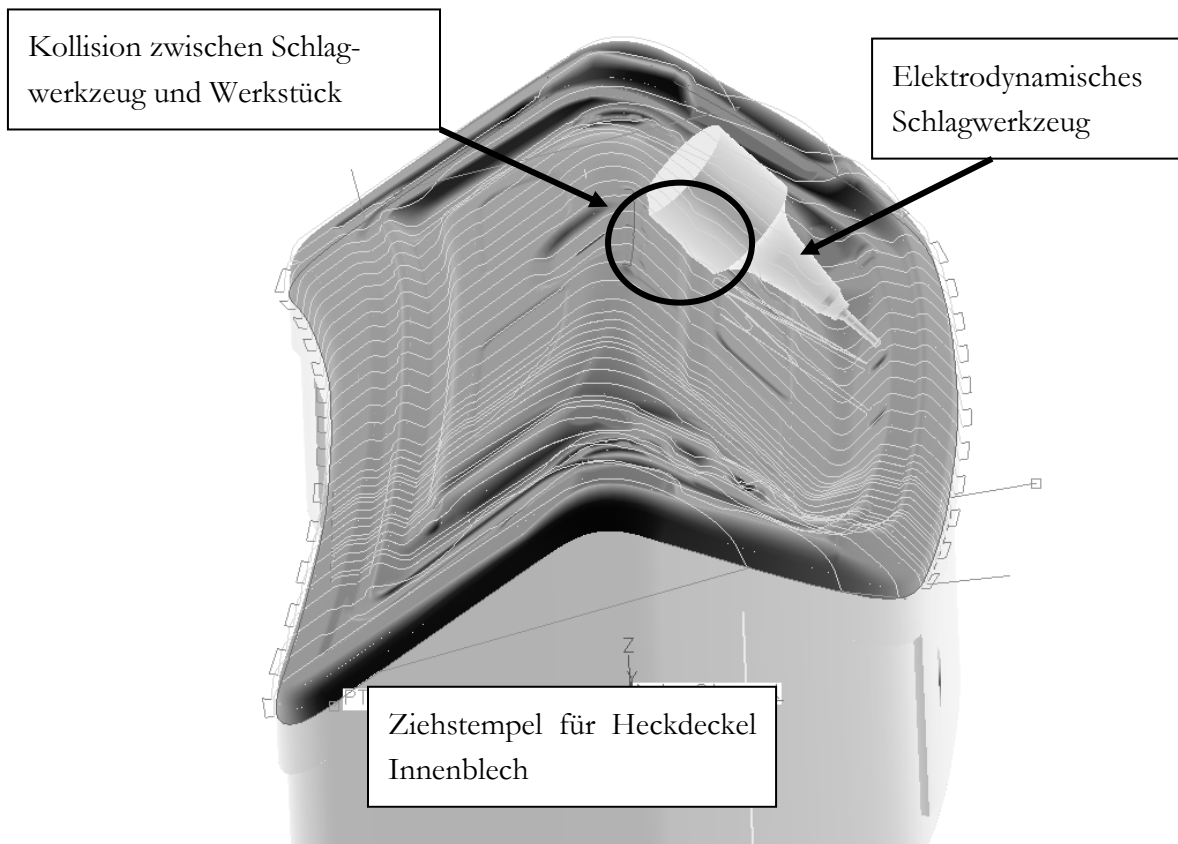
Kollision zwischen Werkzeug und Werkstück bei flächennormaler Bearbeitung
